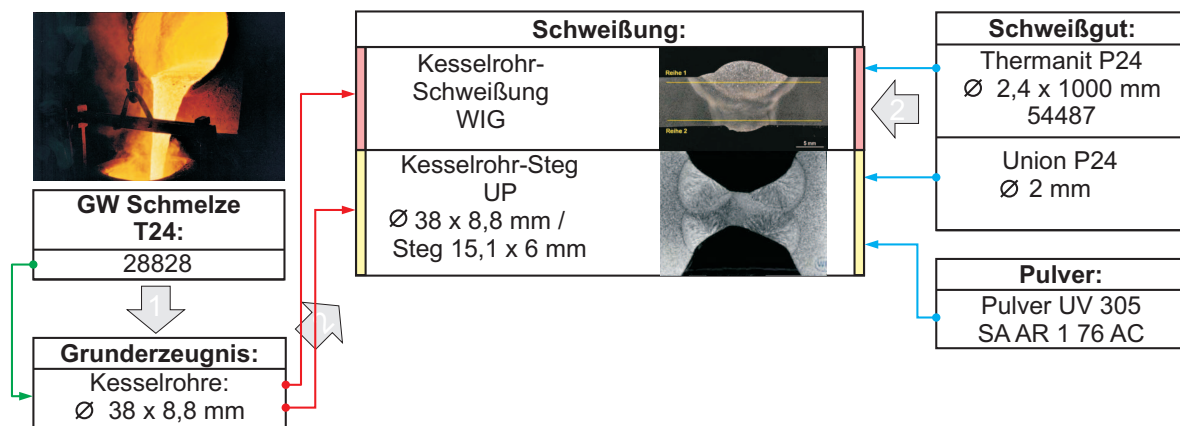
Übersicht der Erzeugnisse, Schmelzen und verwendeten Schweißgüter des Werkstoffes T24
